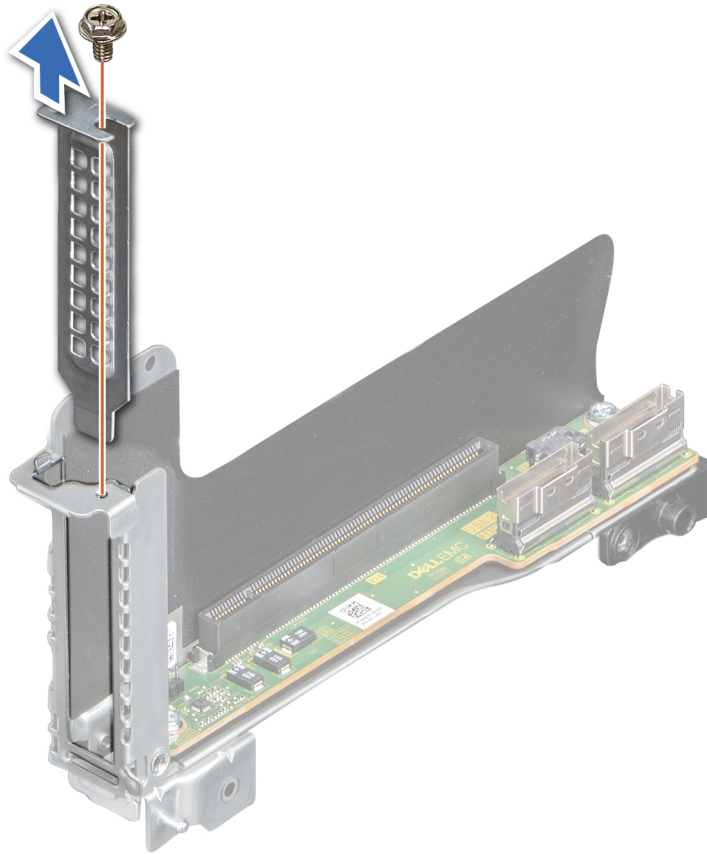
Retrait du support de la plaque de recouvrement de carte d'extension
